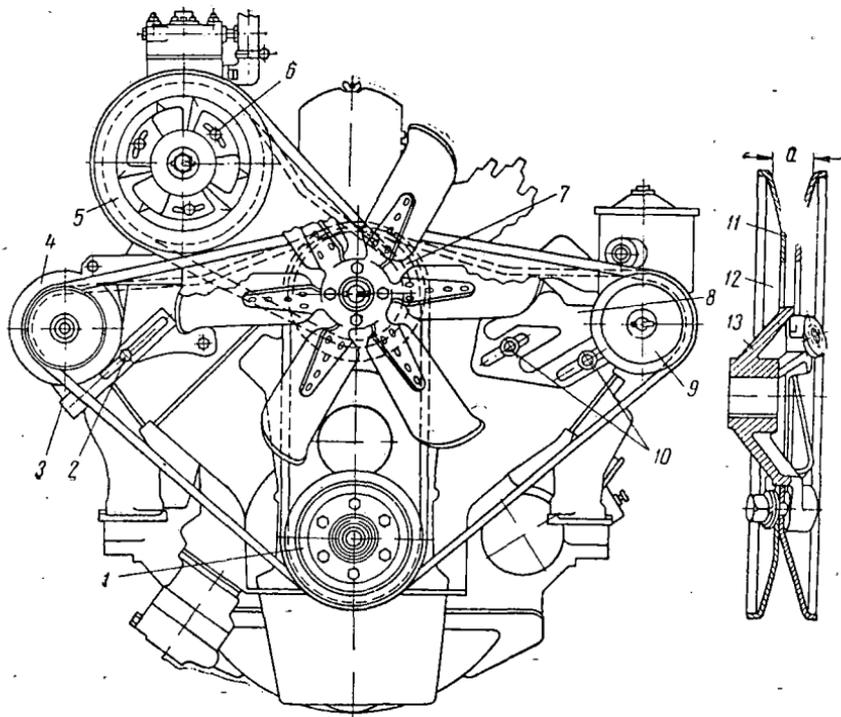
Шкивы и приводные ремни двигателя ЗИЛ-130:
